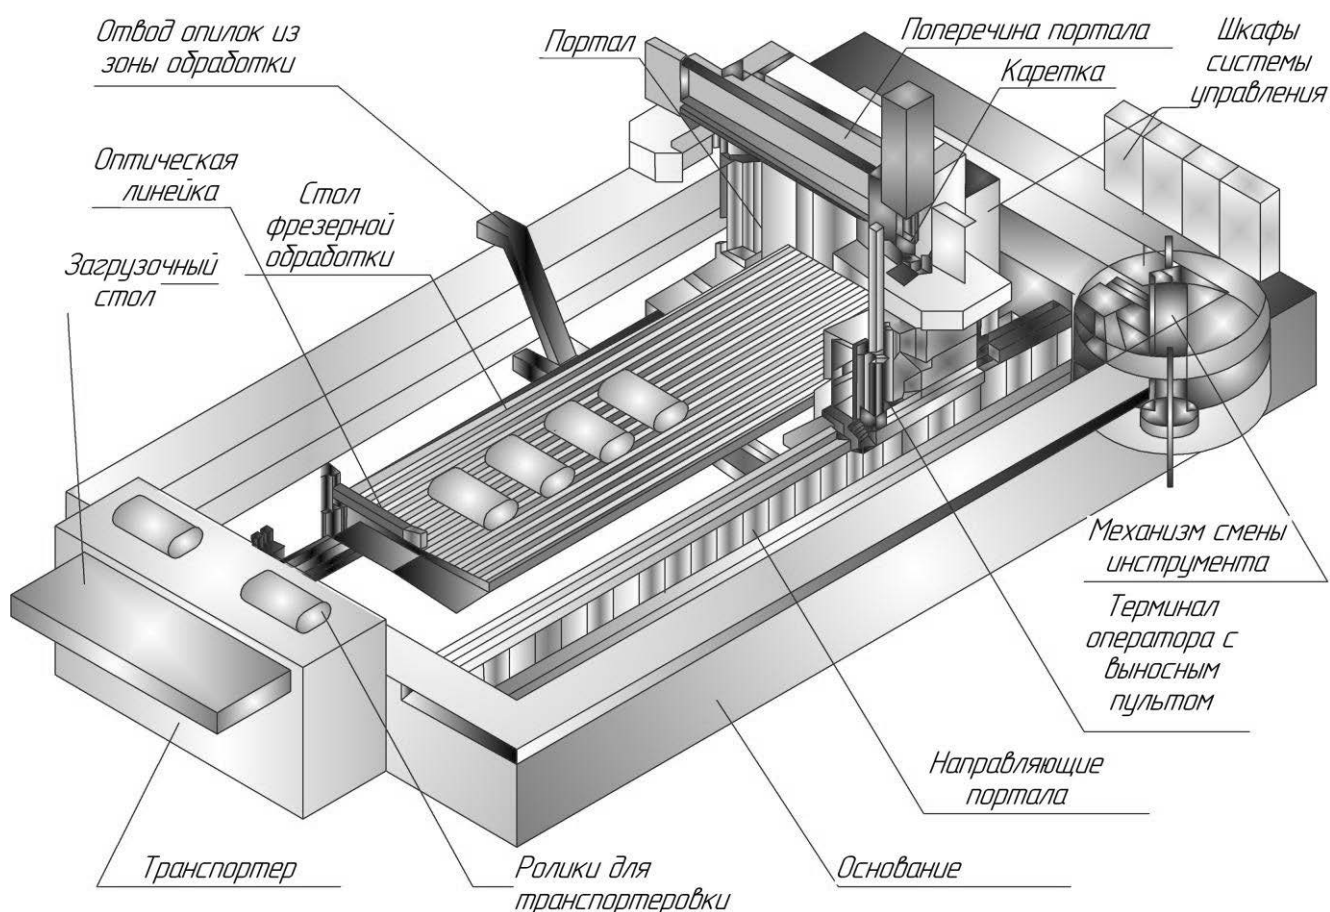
Конструктивно-компоновочная схема ДЦ
